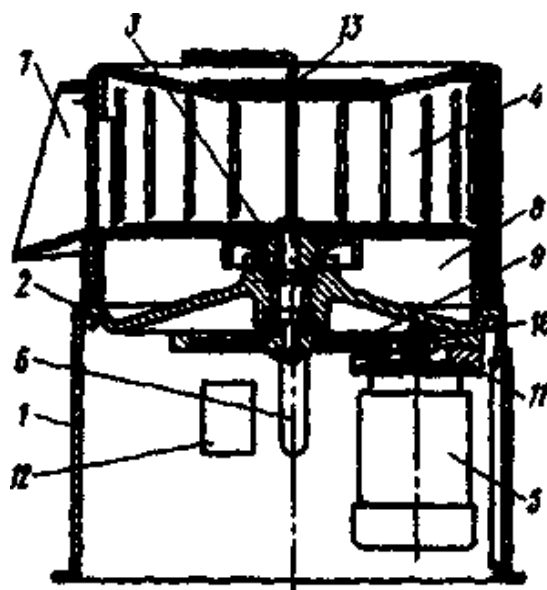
Центрифуга для обробки субпродуктів типу МОС-ЗС (МОС-ЗШ): 1 – станина; 2 – жолоб; 3 – ротор, 4 – барабан, 5 – електродвигун; 6 – патрубок зливний, 7 – люк для вивантаження; 8 – шторка, 9 – колесо зубчасте; 10 – шестірня; 11 – плита підмоторна; 12 – дверцята; 13 – кришка
